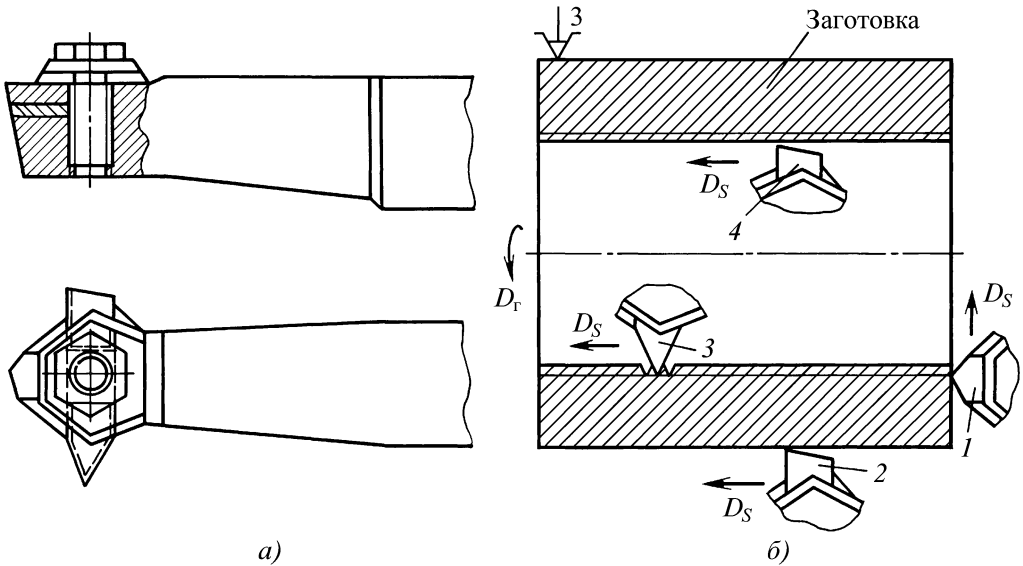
Комбинированный резец со сменными вставками (а) и схема использования (б) его в качестве резца:
